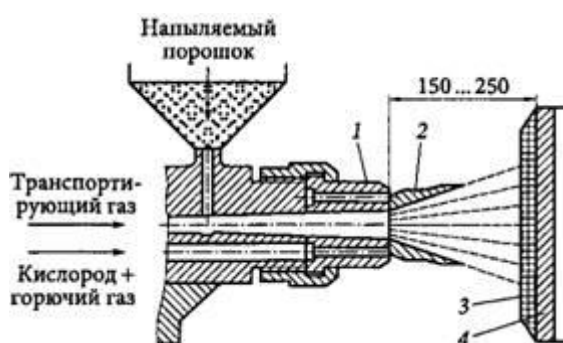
Схема газопламенного напыления транспортирующим газом: 1-сопло; 2 - пламя; 3- покрытие; 4 - напыляемая деталь;
